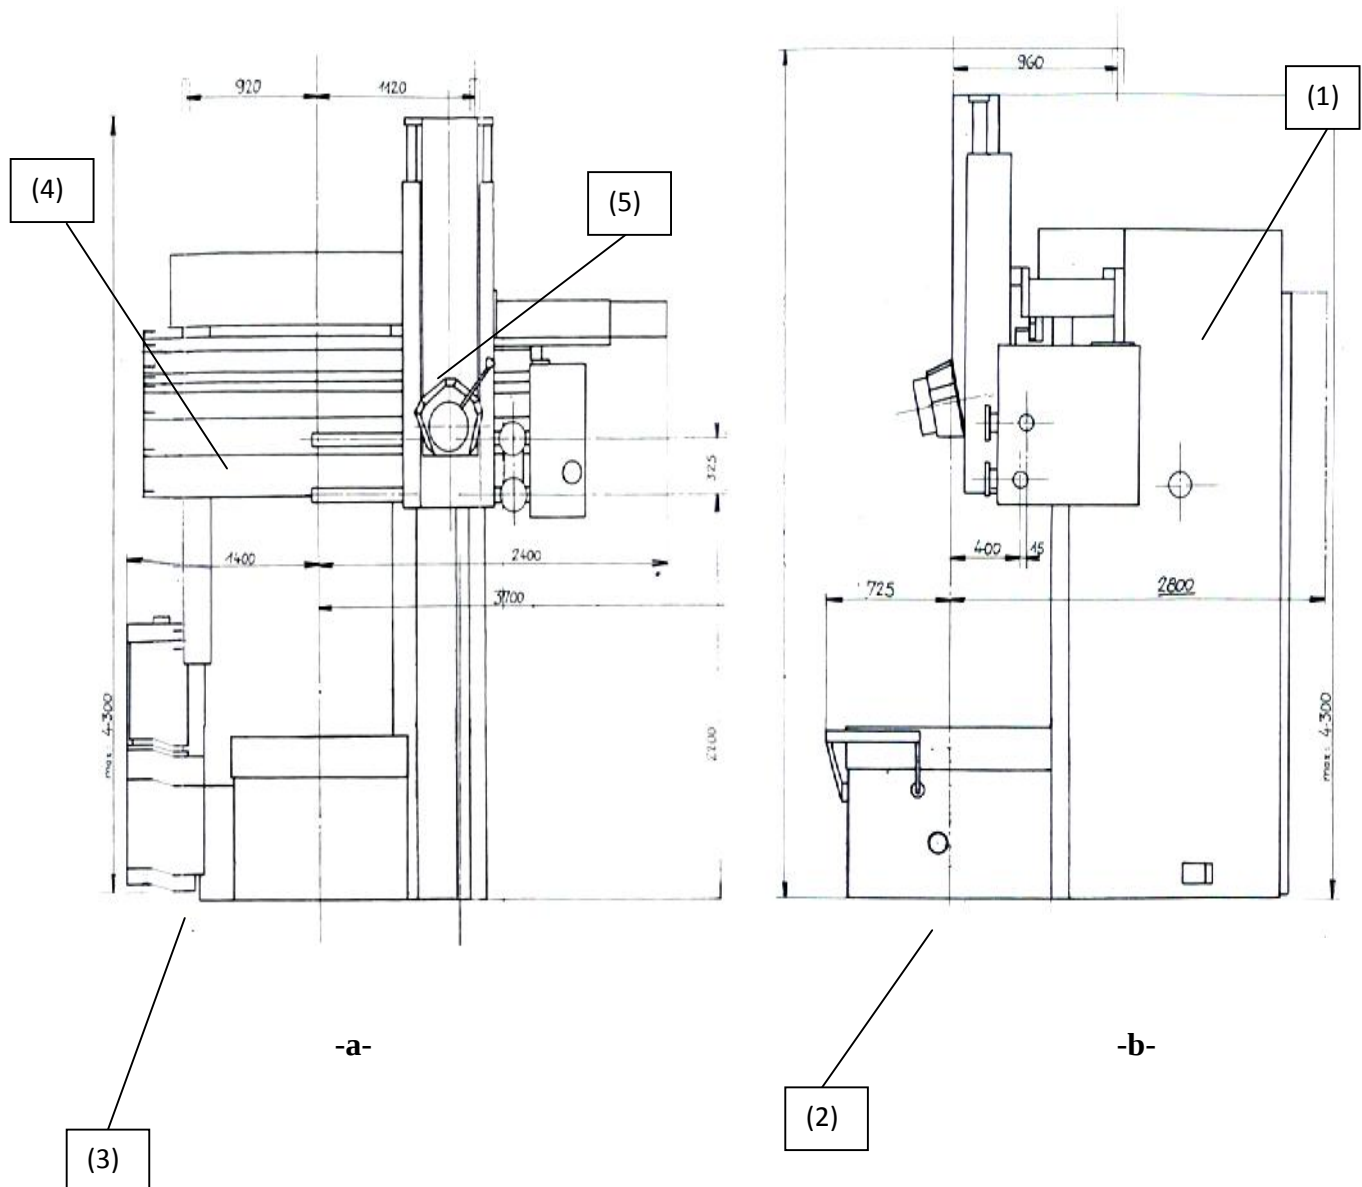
Le tour : (a) vue de face, (b) vue de profil.
